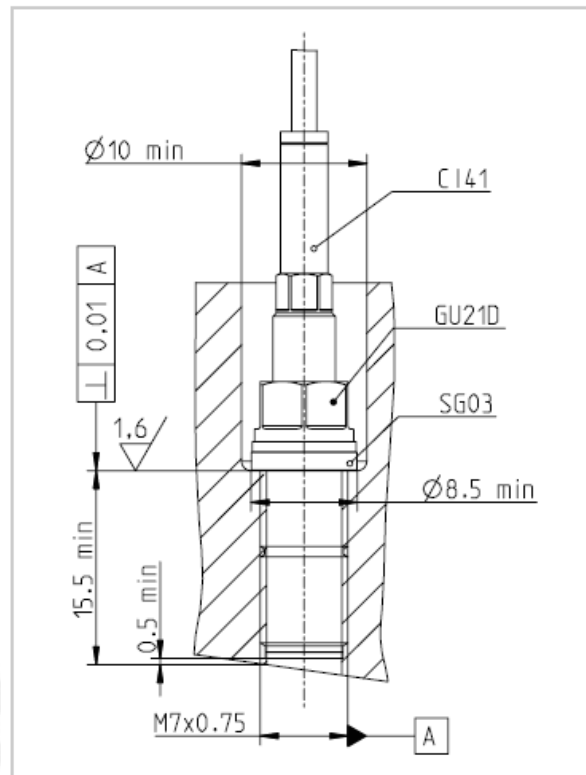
Tolerancias recomendadas para el montaje del sensor de presión.
